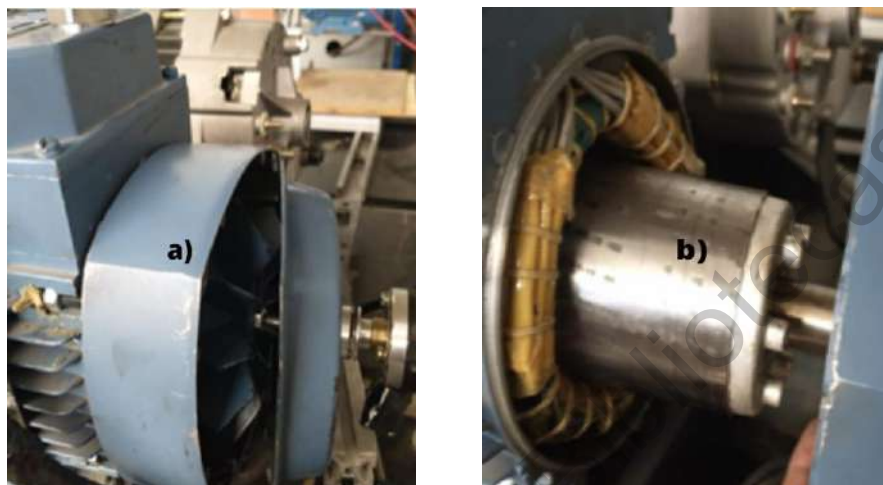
Proceso de desensamblado del motor a) Carcasa b) Rotor (Autoría Propia).
